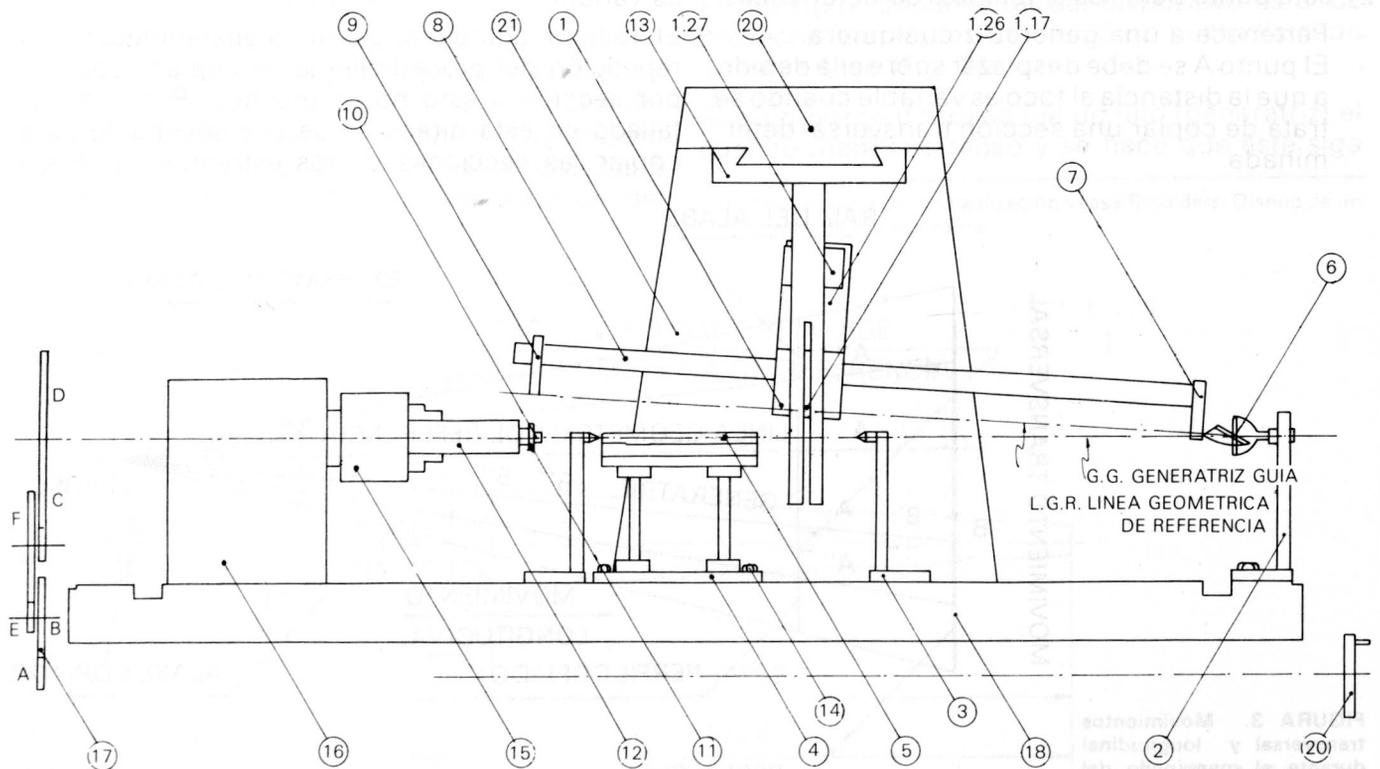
Esquema del dispositivo instalado en la máquina fresadora, escala 1:5.
